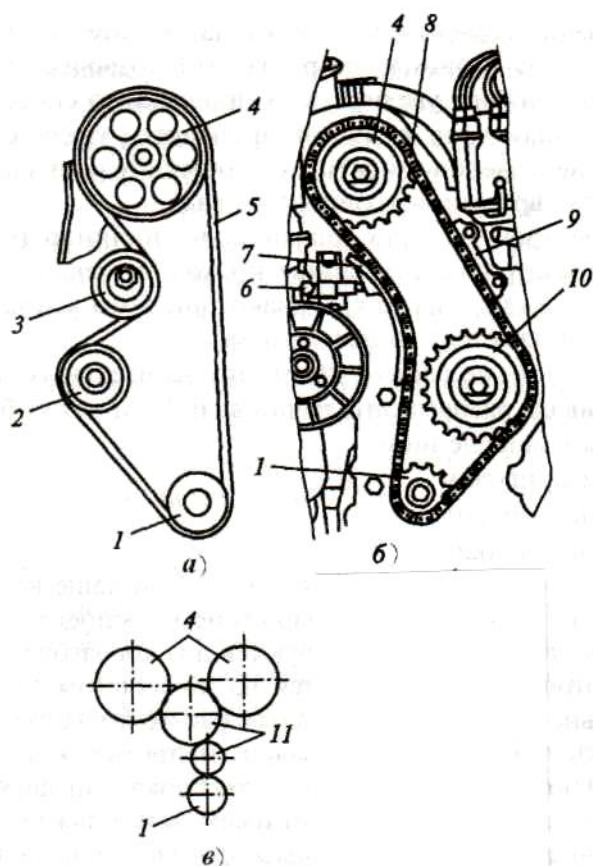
Различные способы привода распределительного вала: а — ременный; б — цепной; в — с зубчатым зацеплением: 1 — коленчатый вал; 2 — жидкостной насос; 3 — натяжной ролик; 4 — распределительный вал; 5 — приводной ремень; 6 — натяжитель цепи; 7 — башмак натяжителя цепи; 8 — цепь; 9 — успокоитель цепи; 10 — масляный насос; 11 — промежуточный вал
